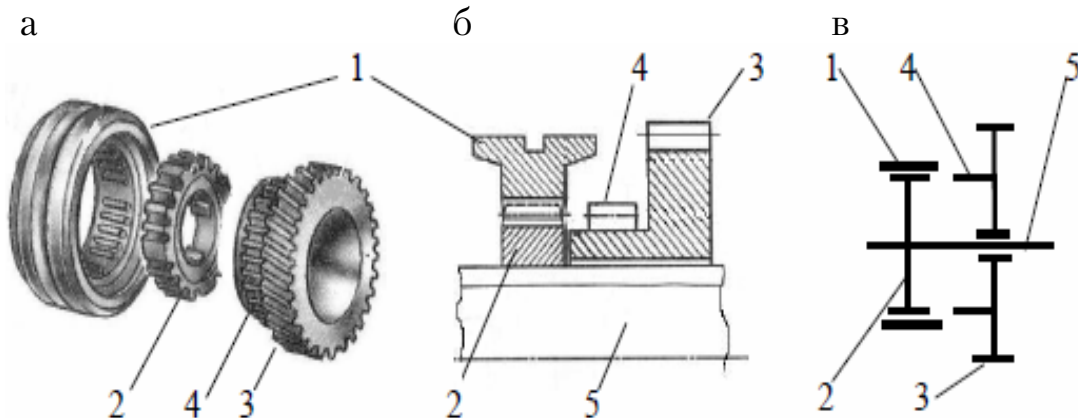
Зубчатая муфта для включения передач в вальной КПП: а – детали; б – чертеж; в – кинематическая схема; 1 – муфта; 2 – ступица; 3 – шестерня включаемой передачи; 4 – зубчатый венец полушестерни включаемой передачи; 5 – ведомый вал
